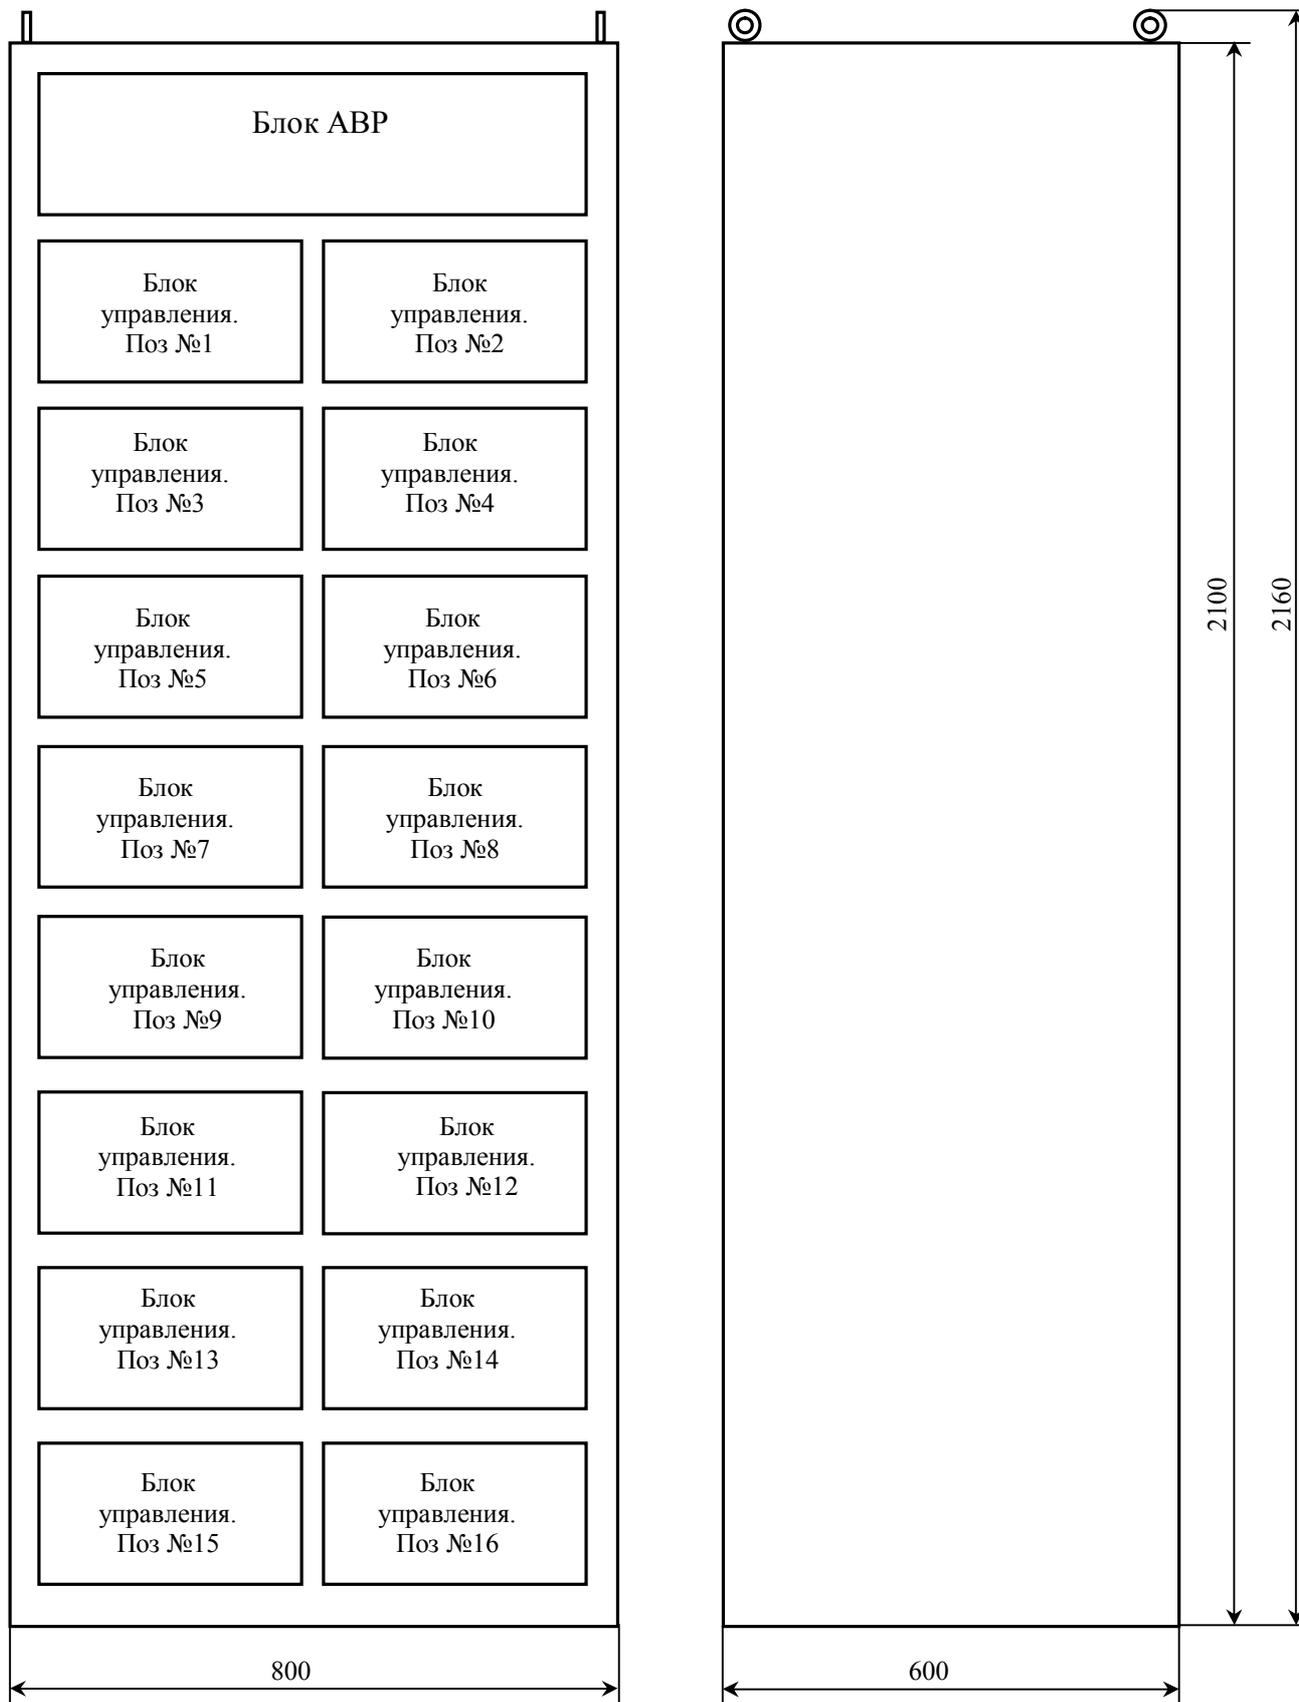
Габаритные и установочные размеры шкафа ШУЭ-16.
